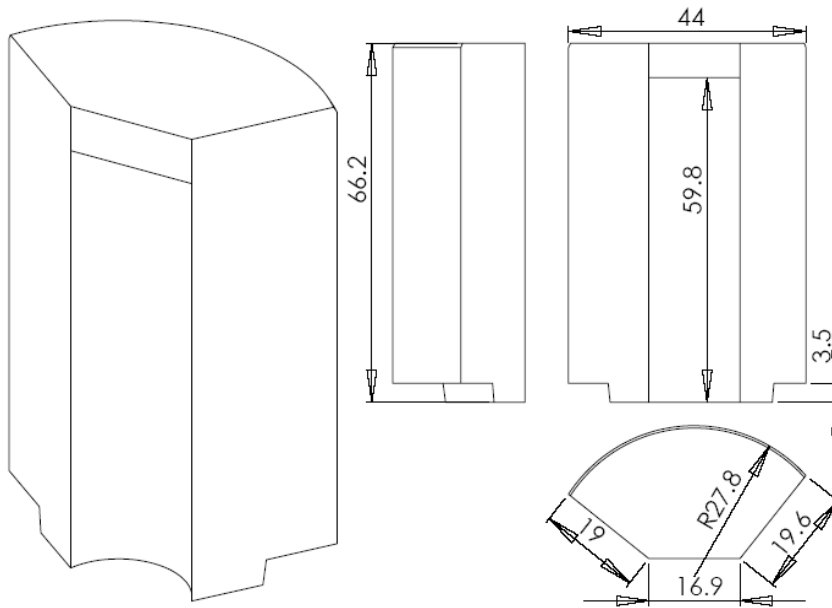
Pieza mecánica industrial - Cámara inicial
